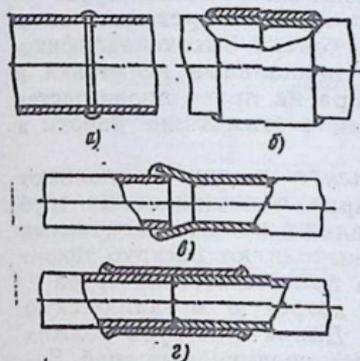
Способы сварки стальных труб встык (а) и с помощью муфты (б) и способы пайки труб из цветных металлов врасстроб с развальцовкой (в) и встык с помощью муфты (г)
